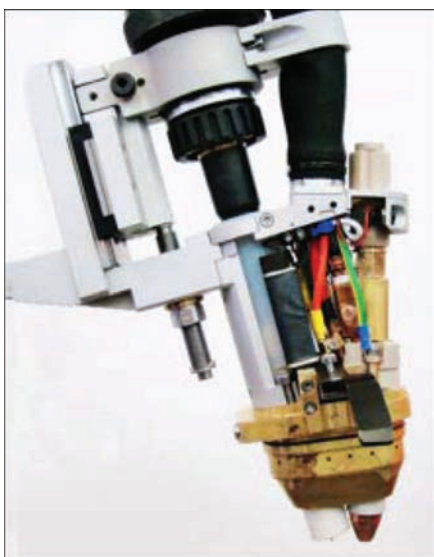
Гибридная горелка фирмы Plasma Laser Technologies Ltd для плазменно-дуговой сварки плавящимся электродом алюминиевых сплавов
